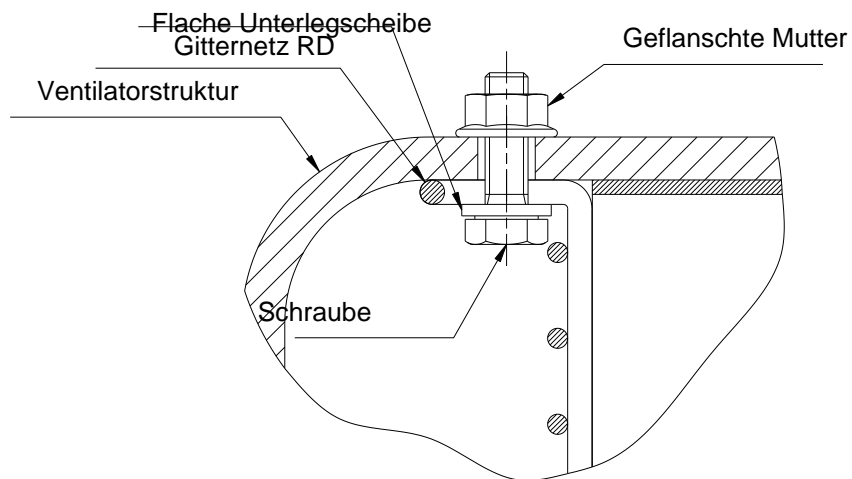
Montageplan der Schutzeinrichtung RD
